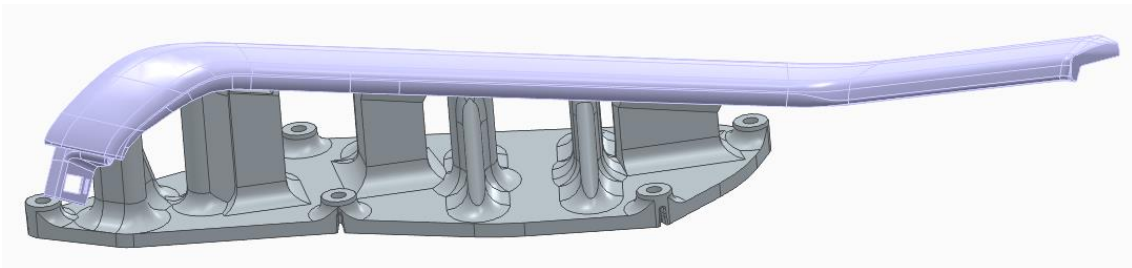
Módulo 1 del utillaje 3 con pieza de trabajo incorporada
